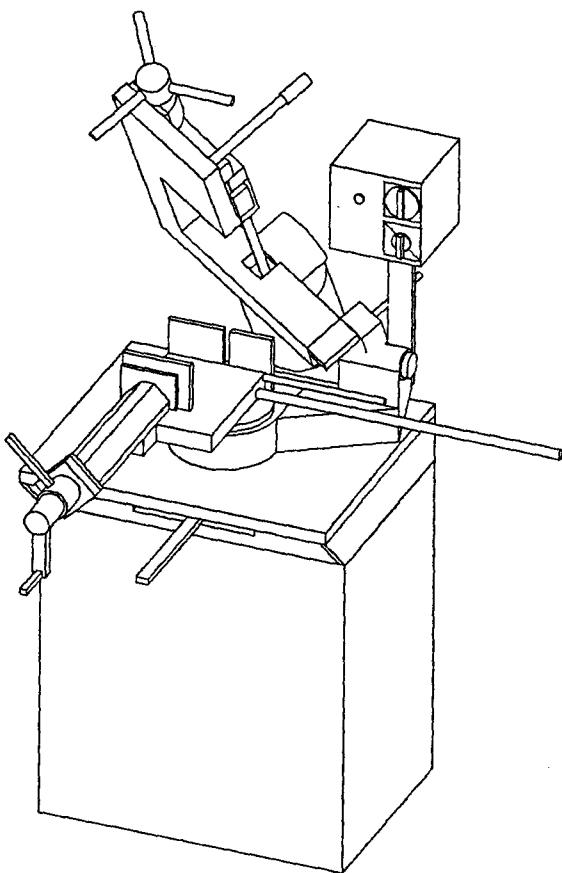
Горизонтальний стрічковопиляльний верстат з хитною головкою
